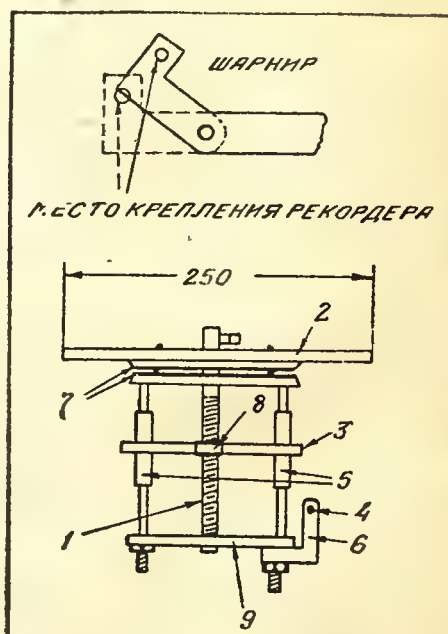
Смещающий механизм: 1 — смещающий винт с шагом резьбы в 1 мм, диаметр винта 9 мм; 2 — диск фрикционного сцепления; 3 — суппорт, к которому крепится рекордер; 4 — держатель адаптера; 5 — направляющие втулки; 6 — отверстия для вилки адаптера; 7 — диски от приемника БЧЗ; 8 — ведущая гайка; 9 — планка, крепящая оси и ведущий винт
